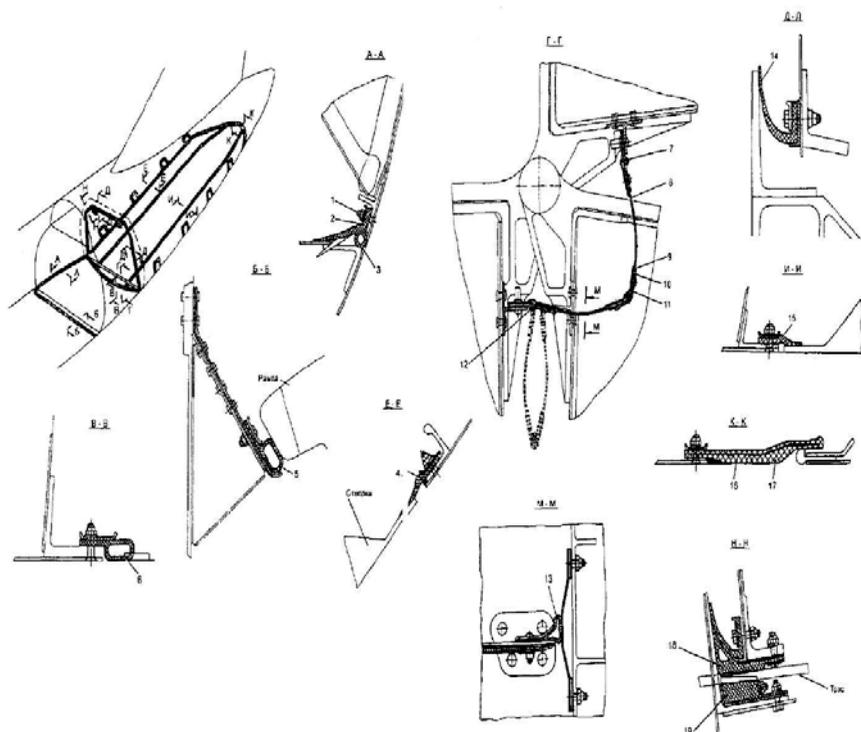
Герметизаторы и уплотнители агрегатов грузового люка
